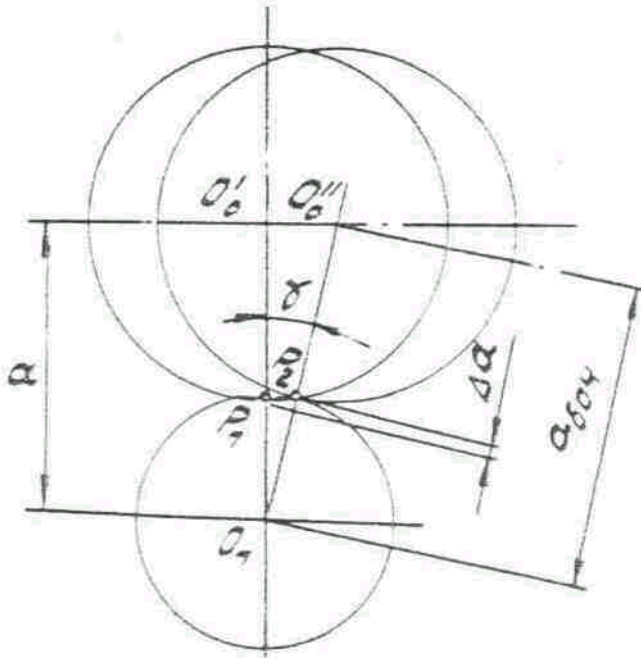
Схема обробки для одержання бочкоподібної модифікації.
